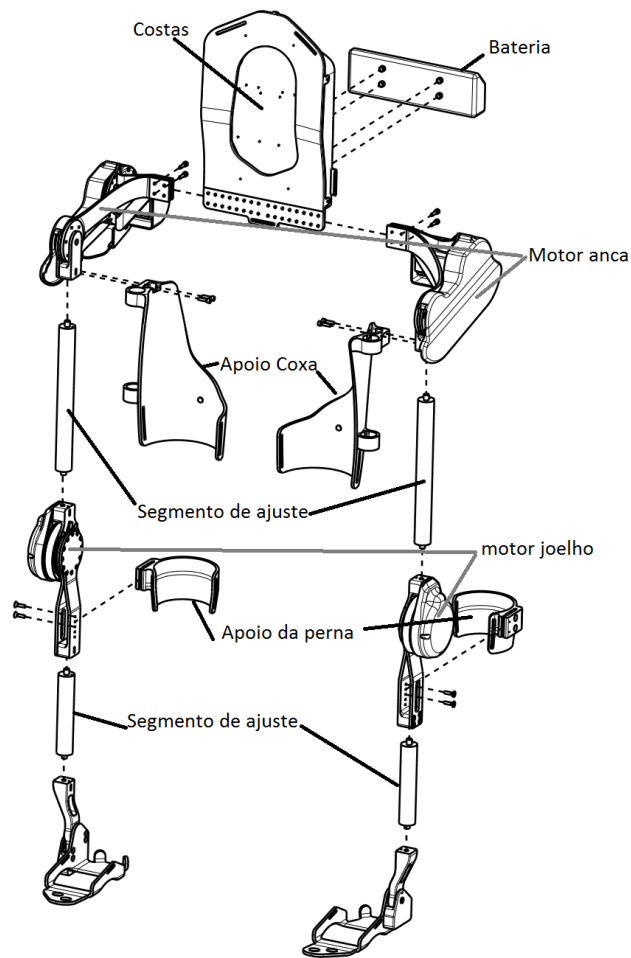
Desenho de montagem dos componentes principais do exoesqueleto
